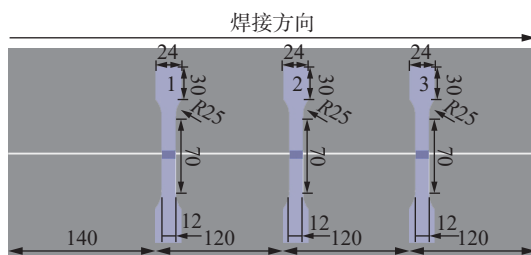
沿焊缝长度方向取样位置示意图 (mm)
